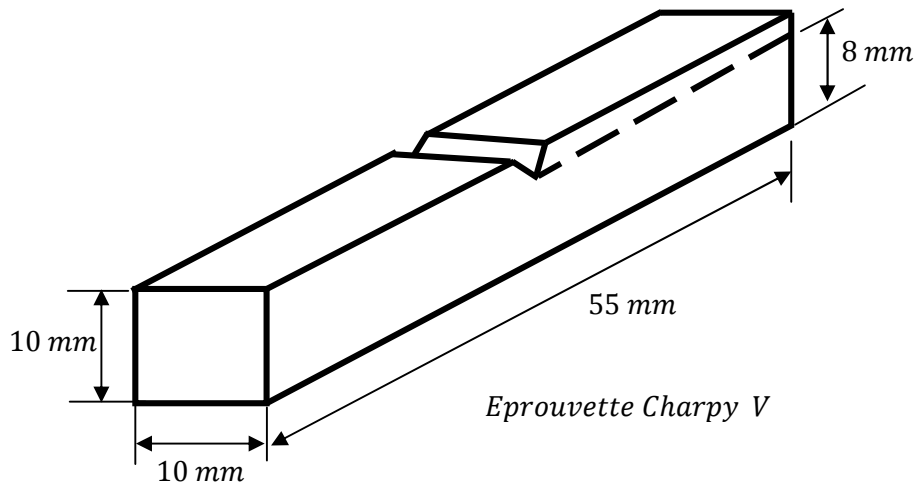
Eprouvettes Charpy standardisées, Les dimensions sont en mm.
